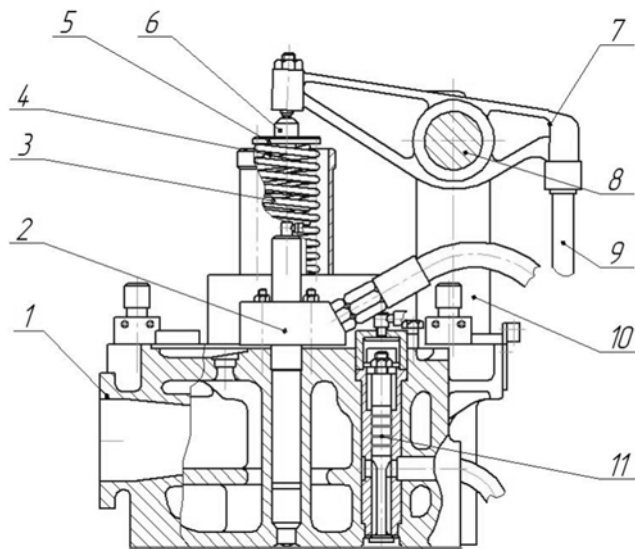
Кришка блоку циліндрів: 1 - корпус головки; 2 - форсунка; 3 - зовнішня пружина клапана; 4 - внутрішня пружина клапану; 5 - верхня тарілка клапану; 6 - клапан; 7 - коромисло; 8 - вісь коромисел; 9 - штанга; 10 - опорна стійка; 11 - повітряний клапан
